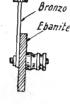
Dettaglio del montaggio per i serrafili A e T.
